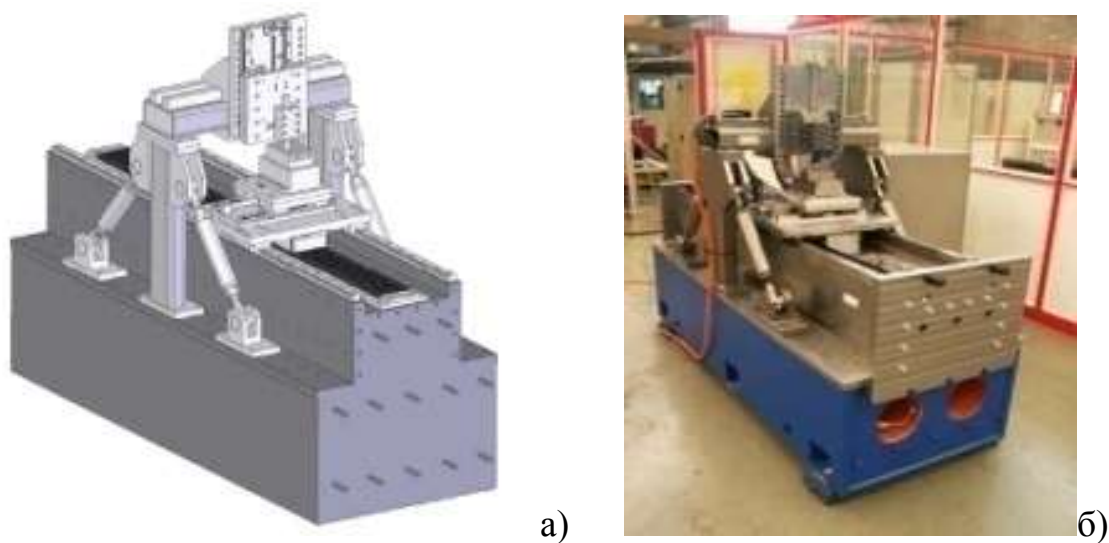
Схема станда (а) і його загальний вигляд (б)
